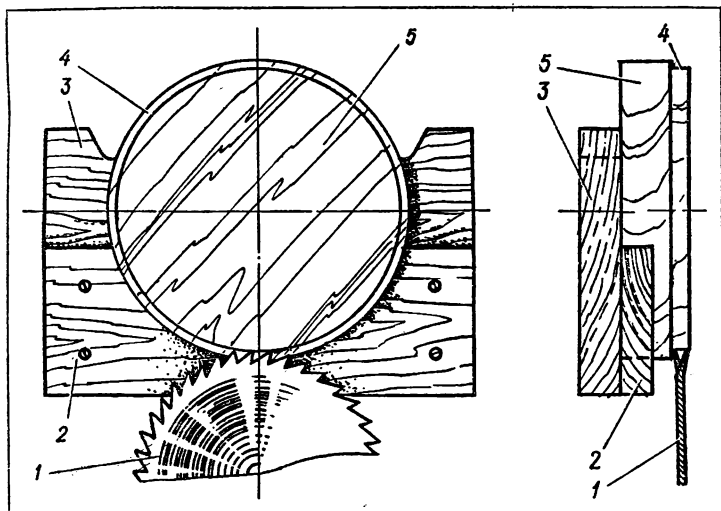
Приспособление для получения кругового уступа на плоскости круга:
